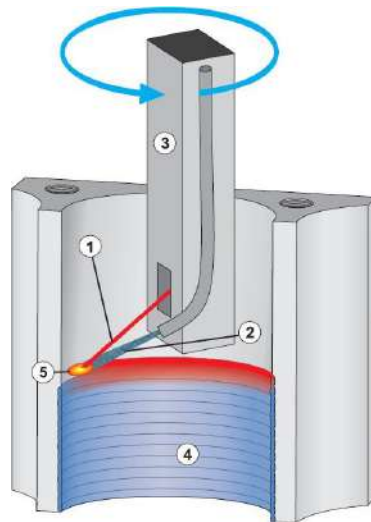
Схематичне зображення процесу лазерного легування поверхні циліндра кремнієм: 1 – лазерний промінь, 2 – струмінь порошку, 3 – лазерний оптичний пристрій, що обертається, 4 – легований шар, 5 – оплавлена зона [21]
